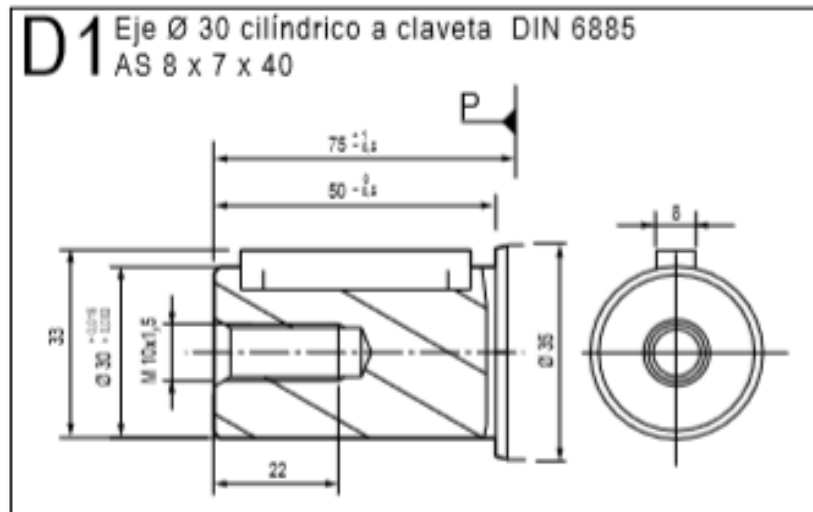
Dimensiones del eje del motor hidráulico.
